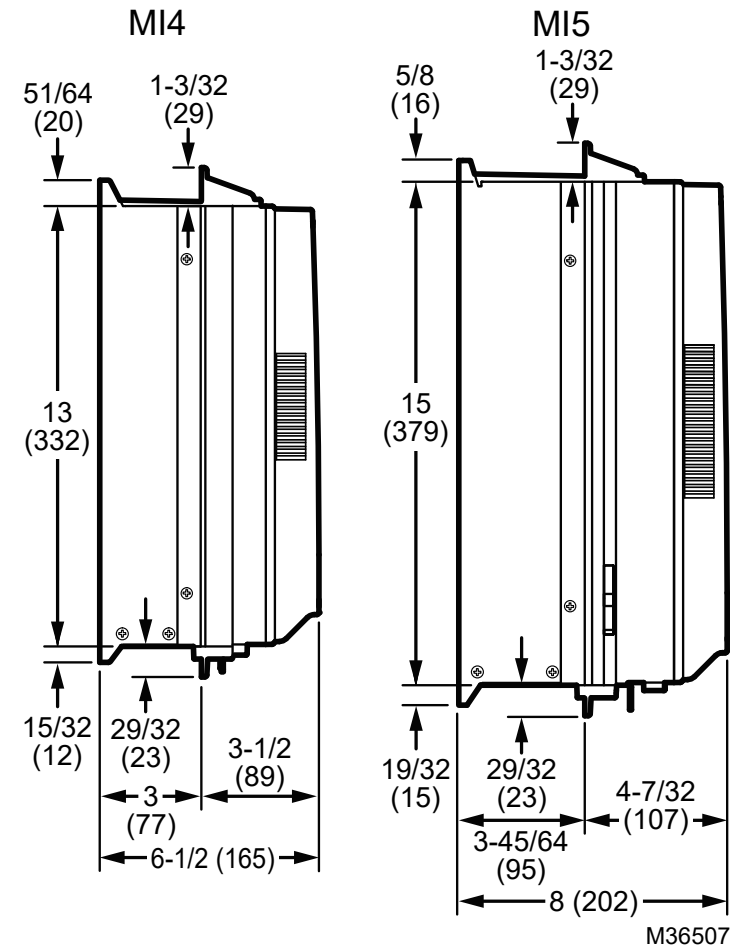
Dimensions de profondeur en montage par bride, pour MI4 et MI5 [unité : pouces (mm)]
